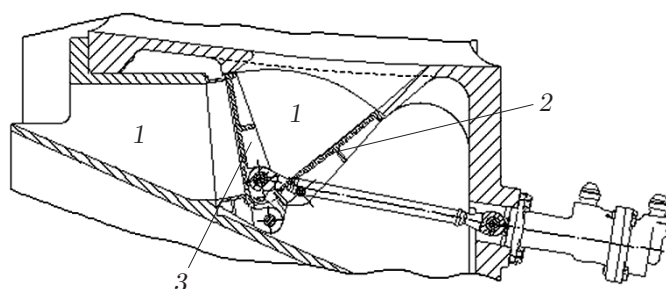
Схема заслонки канала перепуска из подпорной ступени компрессора низкого давления во внешний контур двигателя ПС-90А:
